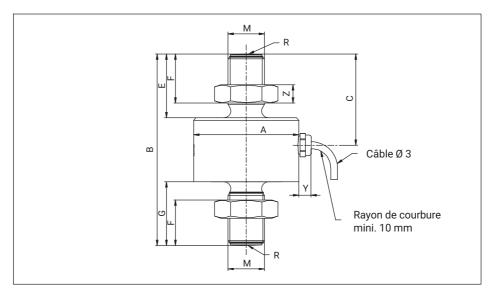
Dimensions U9C 0,5 kN à 50 kN
